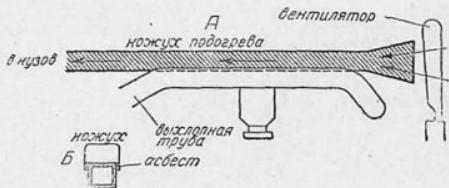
А — схема устройства отопления кузова; Б — разрез выхлопной трубы с укрепленным на ней кожухом
